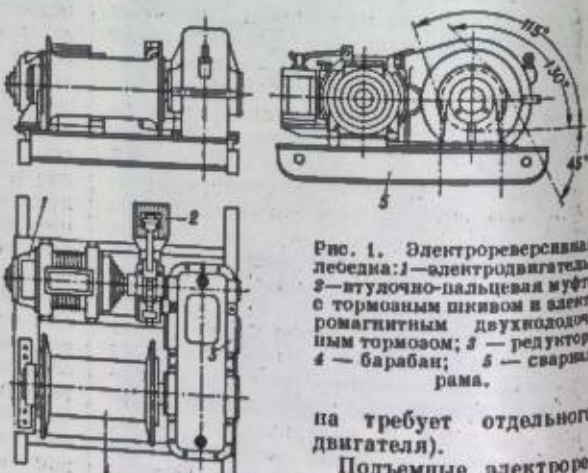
Электрореверсивная лебедка: 1 — электродвигатель; 2 — штурвално-пальцевая муфта с тормозным шкивом и электроромантическим тормозом; 3 — редуктор; 4 — барабан; 5 — сварная рама.
